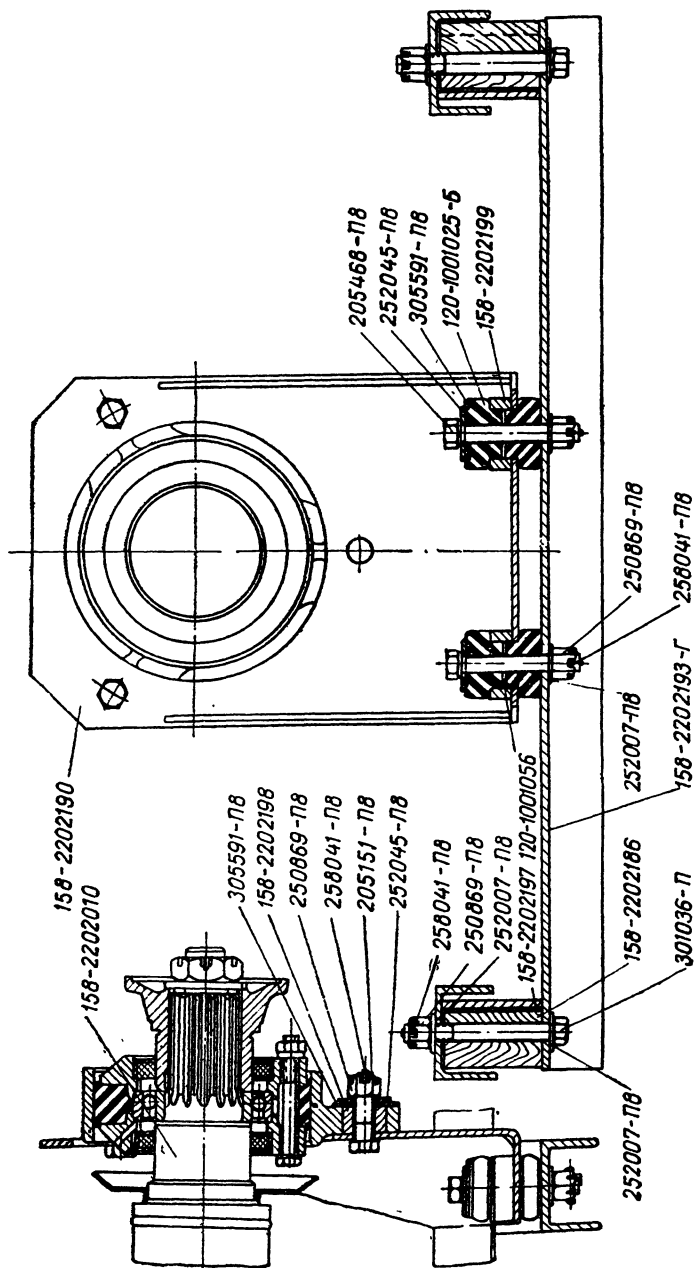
Установка опоры промежуточного карданного вала автобуса ЗИЛ-158
